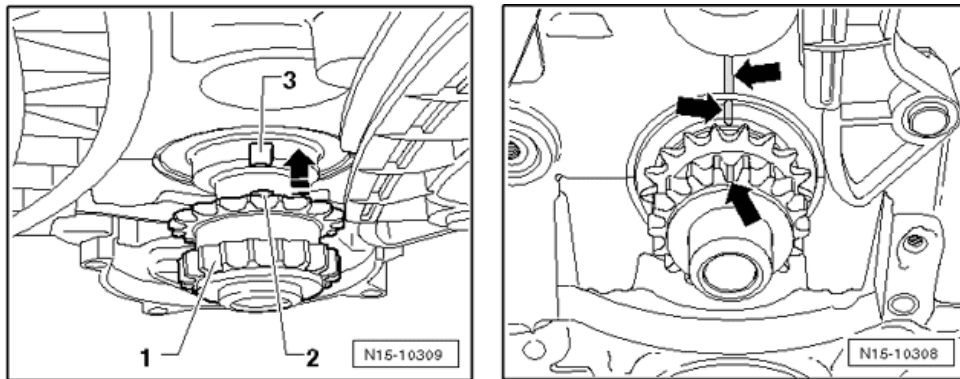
Posição de montagem do pinhão com a cambota.
